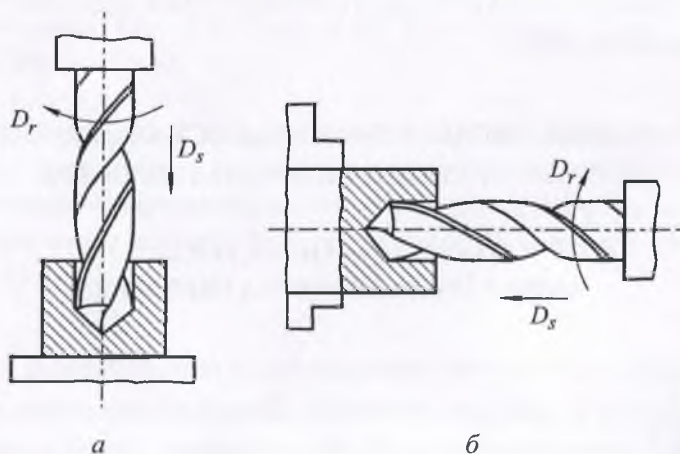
Схемы обработки отверстий на сверлильных (а) и токарных (б) станках
